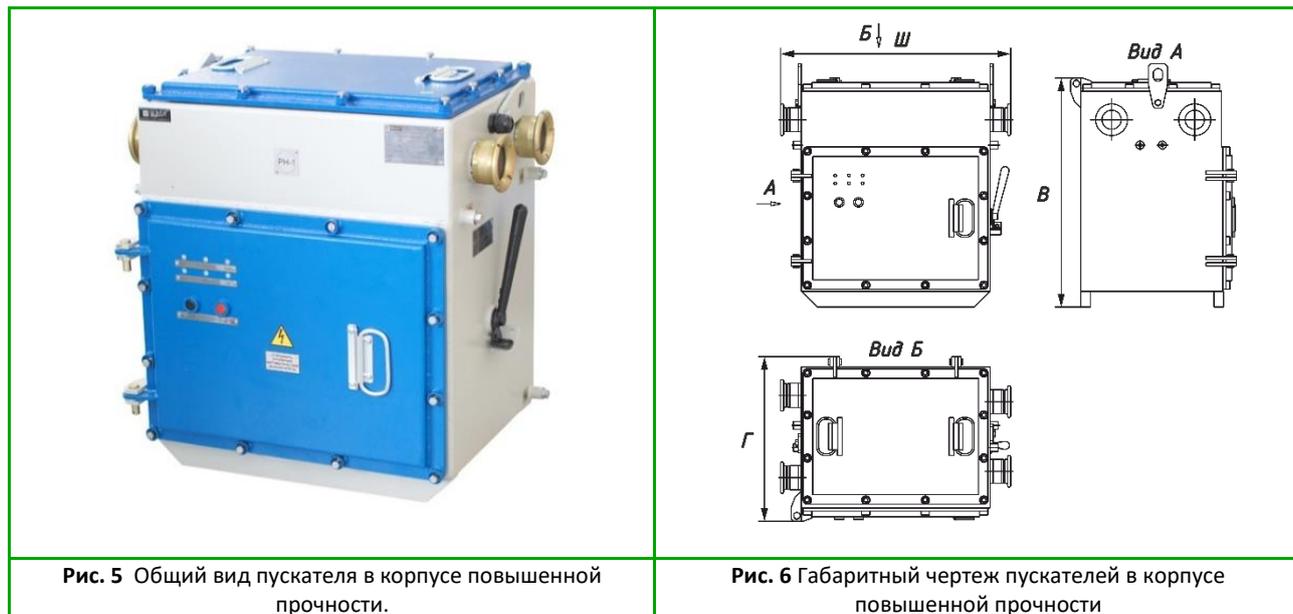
Общий вид пускателя в корпусе повышенной прочности.
